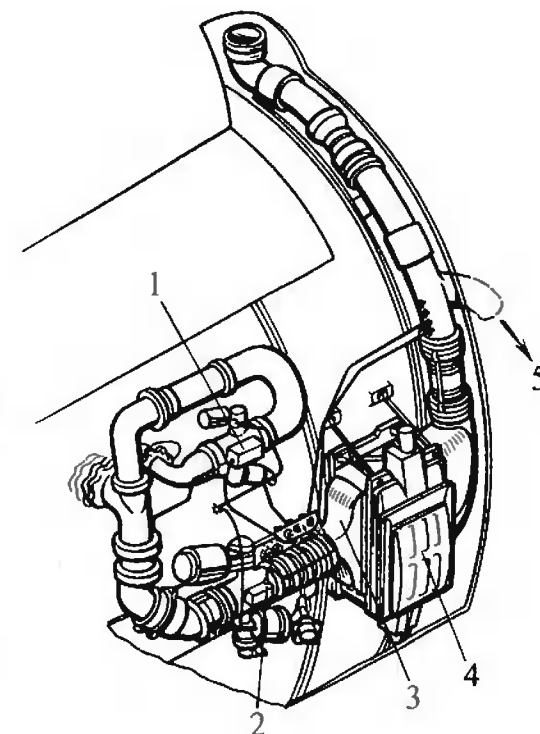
Компоновка подсистемы отбора и предварительной подготовки воздуха на двигателе:
